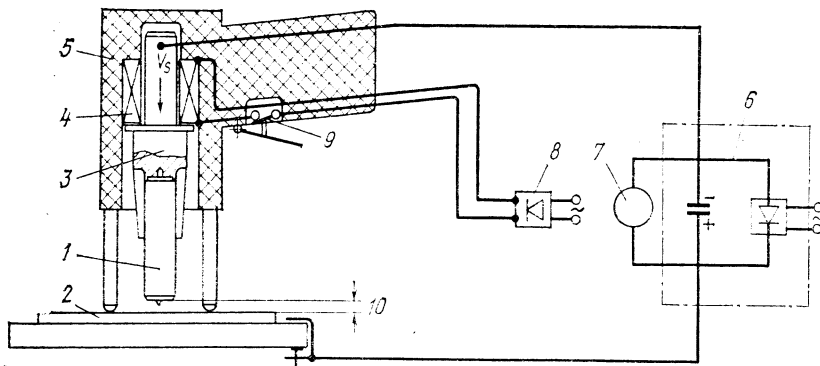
Ударная конденсаторная сварка болтов:
